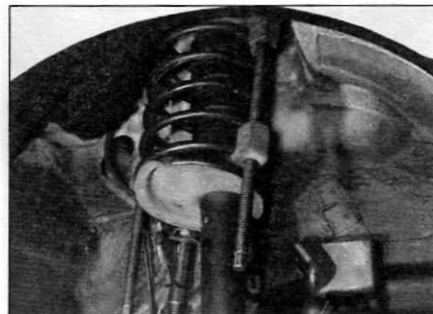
Приспособления для сжатия пружин, установленные на пружину стойки
